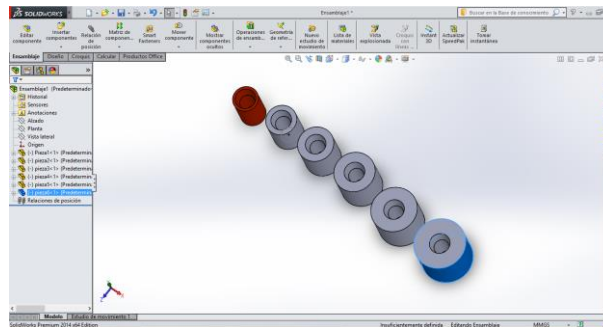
Todas las piezas diseñadas para la torre de Hanoi en SolidWorks.
